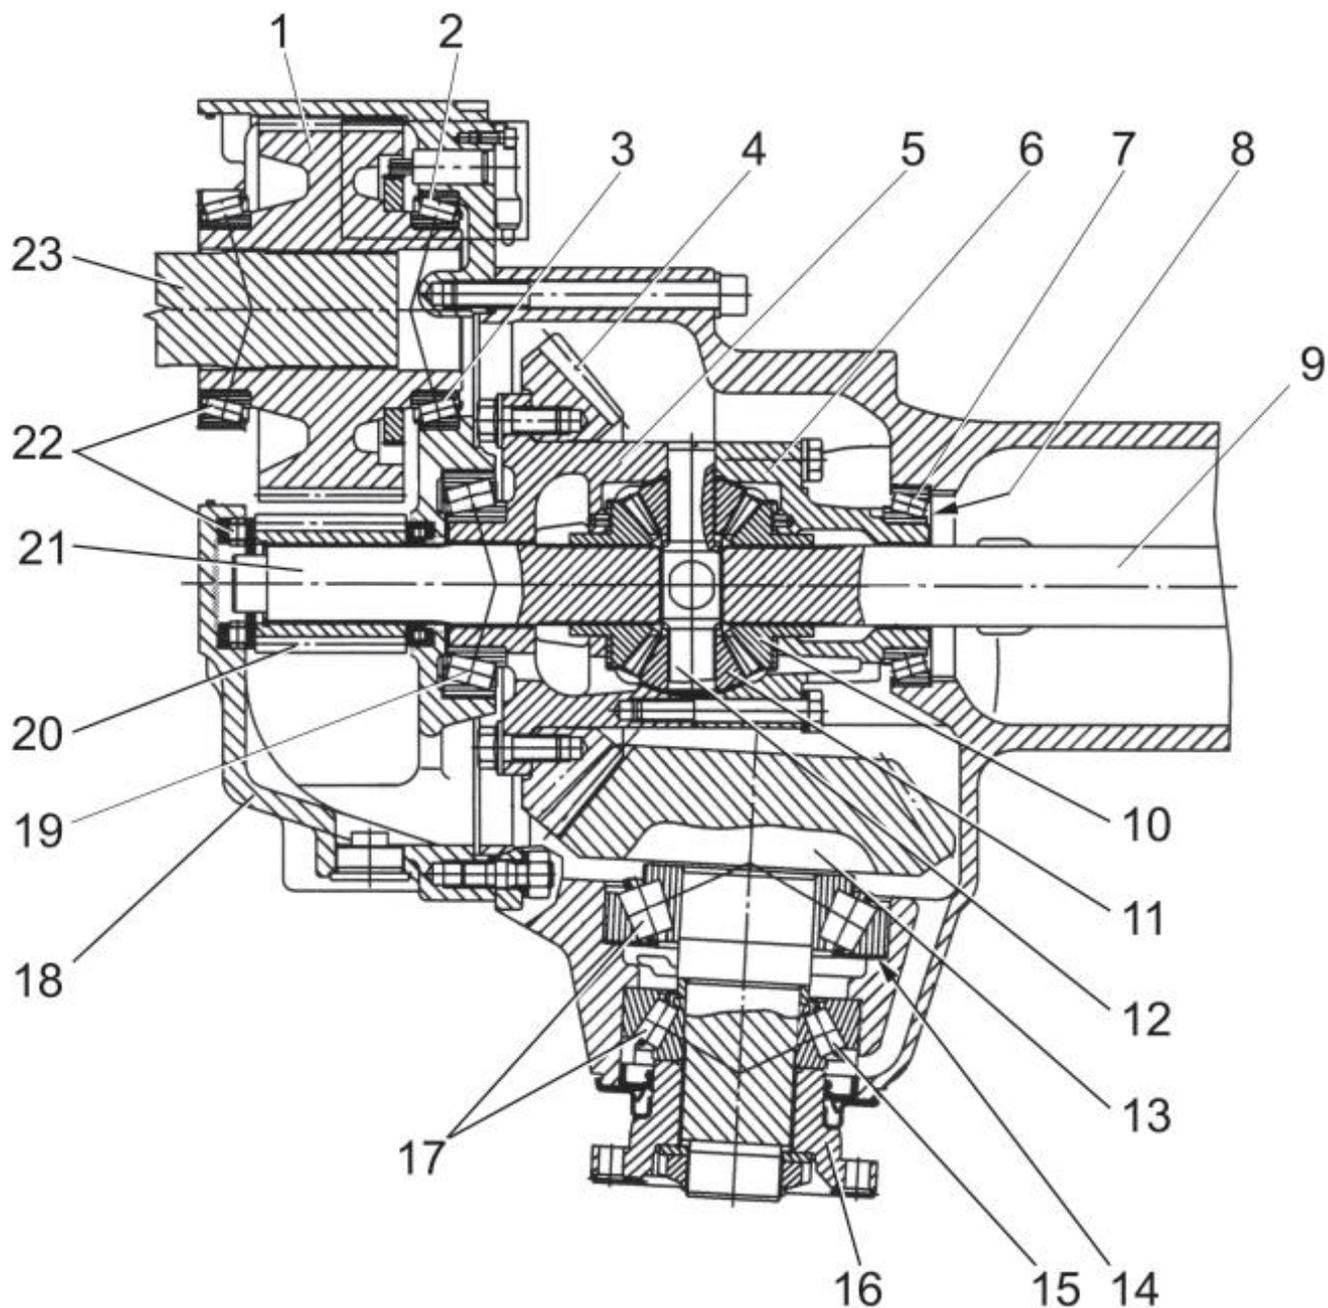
Главная передача (центральный ионический редуктор и дифференциал)
